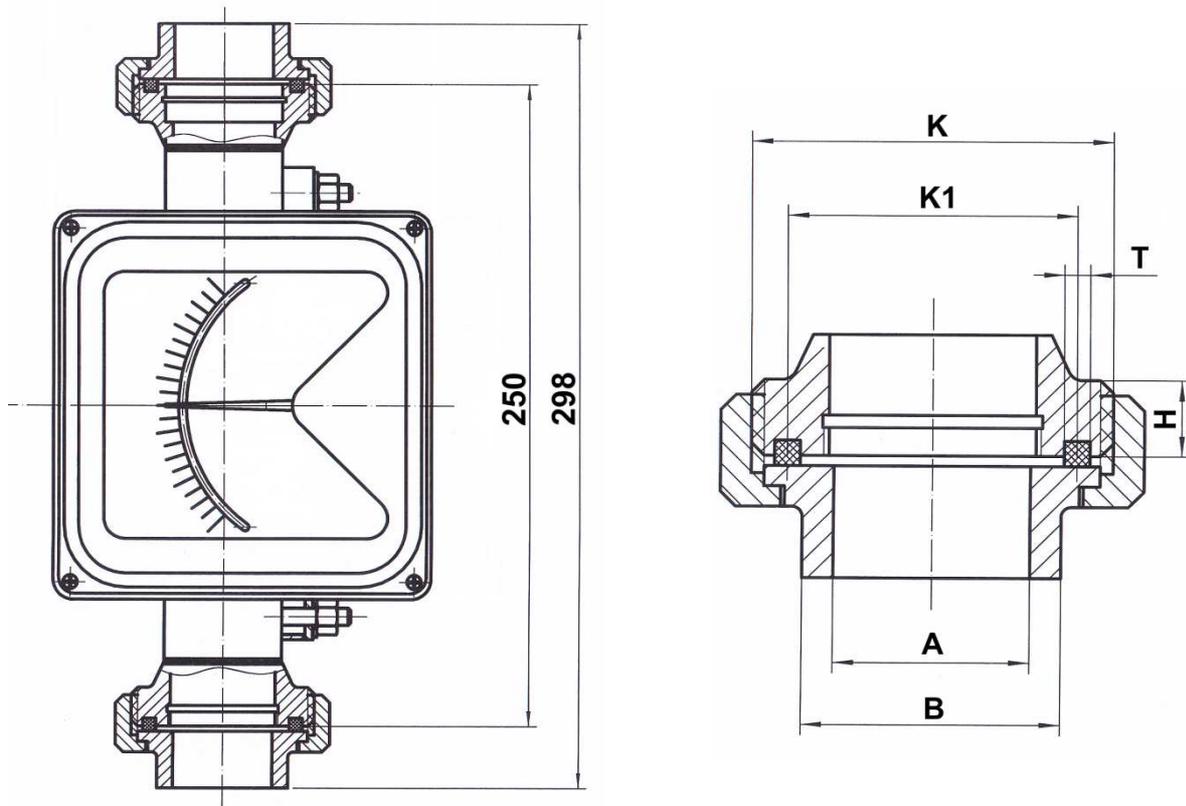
Присоединительные размеры приборов с муфтовым соединением
